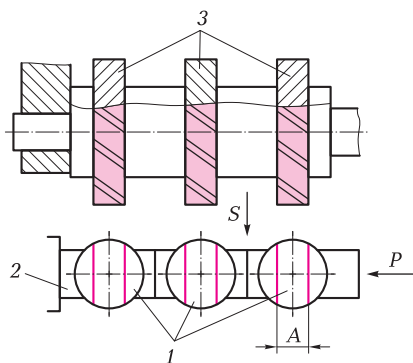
Схема одновременной последовательной обработки заготовки: 1 — режущий инструмент; 2 — заготовки; 3 — приспособление
